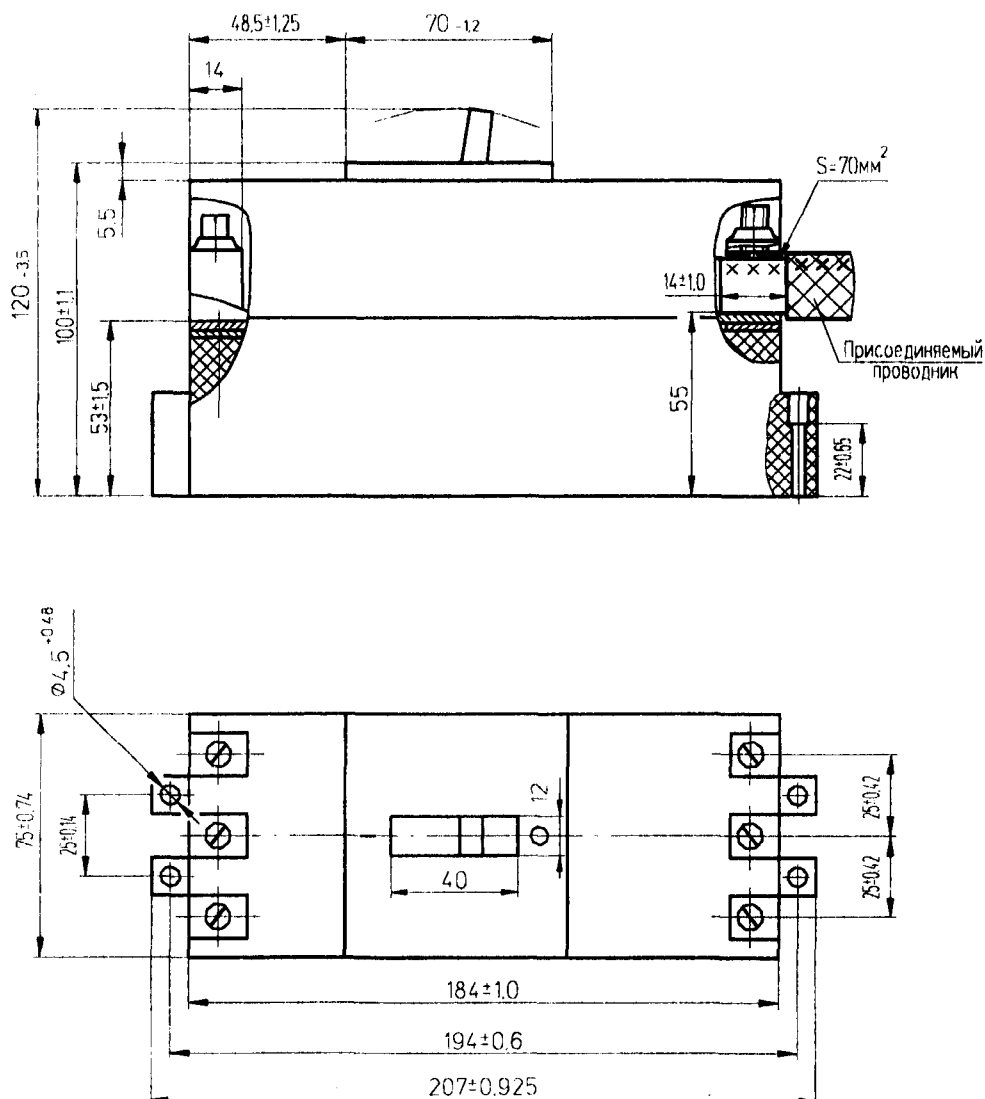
Выводы главных цепей выключателей резьбового типа.
